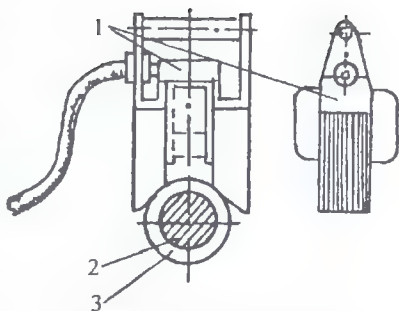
Индуктор для нагрева подшипников на валу: 1 — индуктор; 2 — вал; 3 — подшипник
